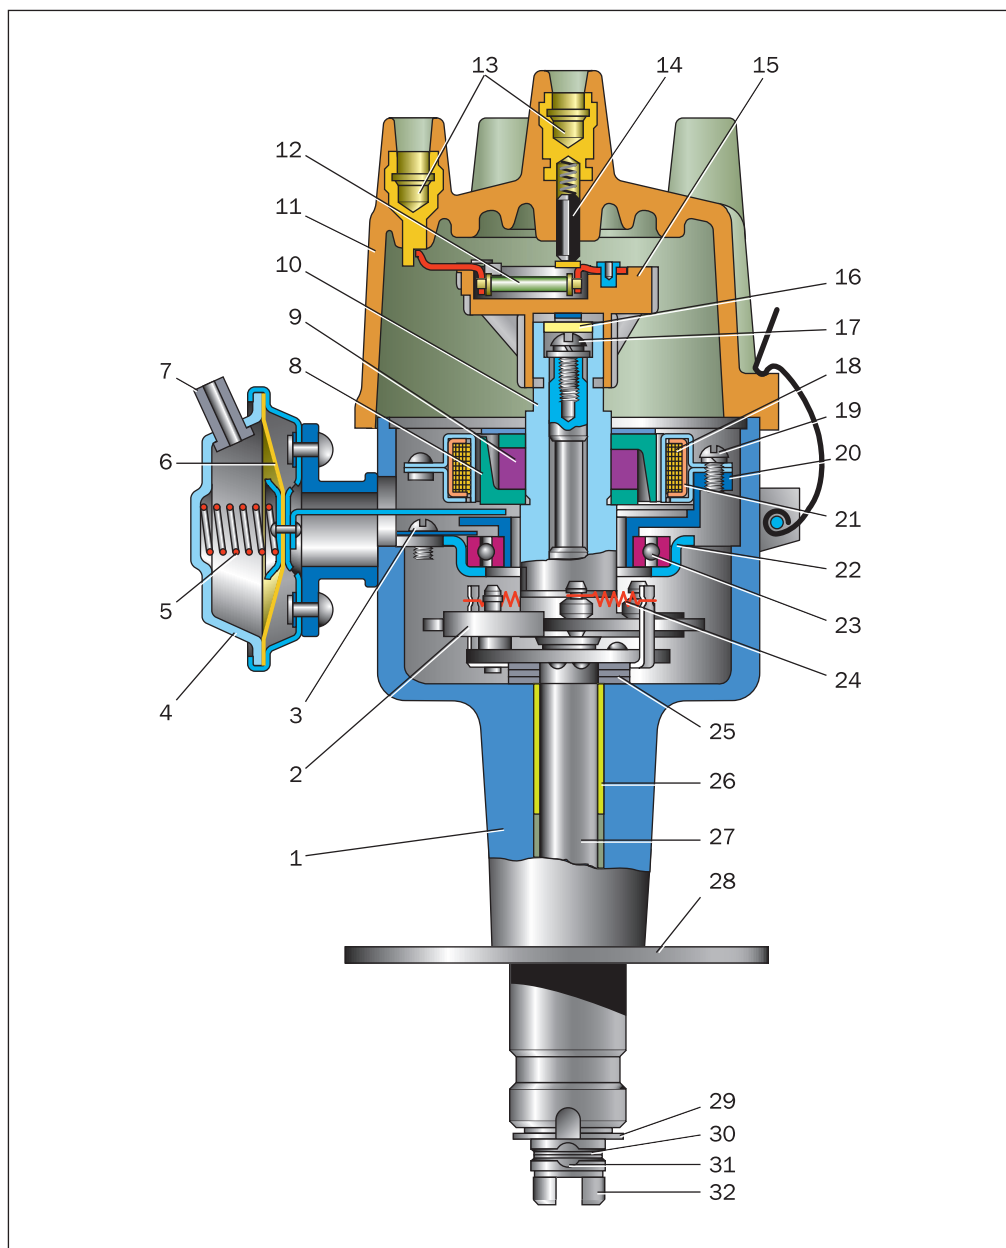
Конструкция датчика-распределителя зажигания: 1 — корпус; 2 — грузик центробежного регулятора; 3 — винт крепления подшипника; 4 — вакуумный регулятор; 5 — пружина вакуумного регулятора; 6 — диафрагма; 7 — штуцер; 8 — магнитопровод ротора; 9 — постоянный магнит; 10 — ротор; 11 — крышка; 12 — помехоподавительный резистор; 13 — выводы; 14 — центральный контакт; 15 — бегунок; 16 — фольц; 17 — винт крепления ротора; 18 — обмотка статора; 19 — винт крепления статора; 20 — статор; 21 — магнитопровод обмотки статора; 22 — опора статора; 23 — подшипник; 24 — пружина грузика; 25 — упорные шайбы; 26 — втулка; 27 — валик; 28 — пластина октан-корректора; 29 — шайба; 30 — пружинное кольцо; 31 — штифт; 32 — муфта привода
